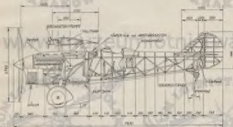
Längsschnitt eines modernen Jagdflugzeuges.
